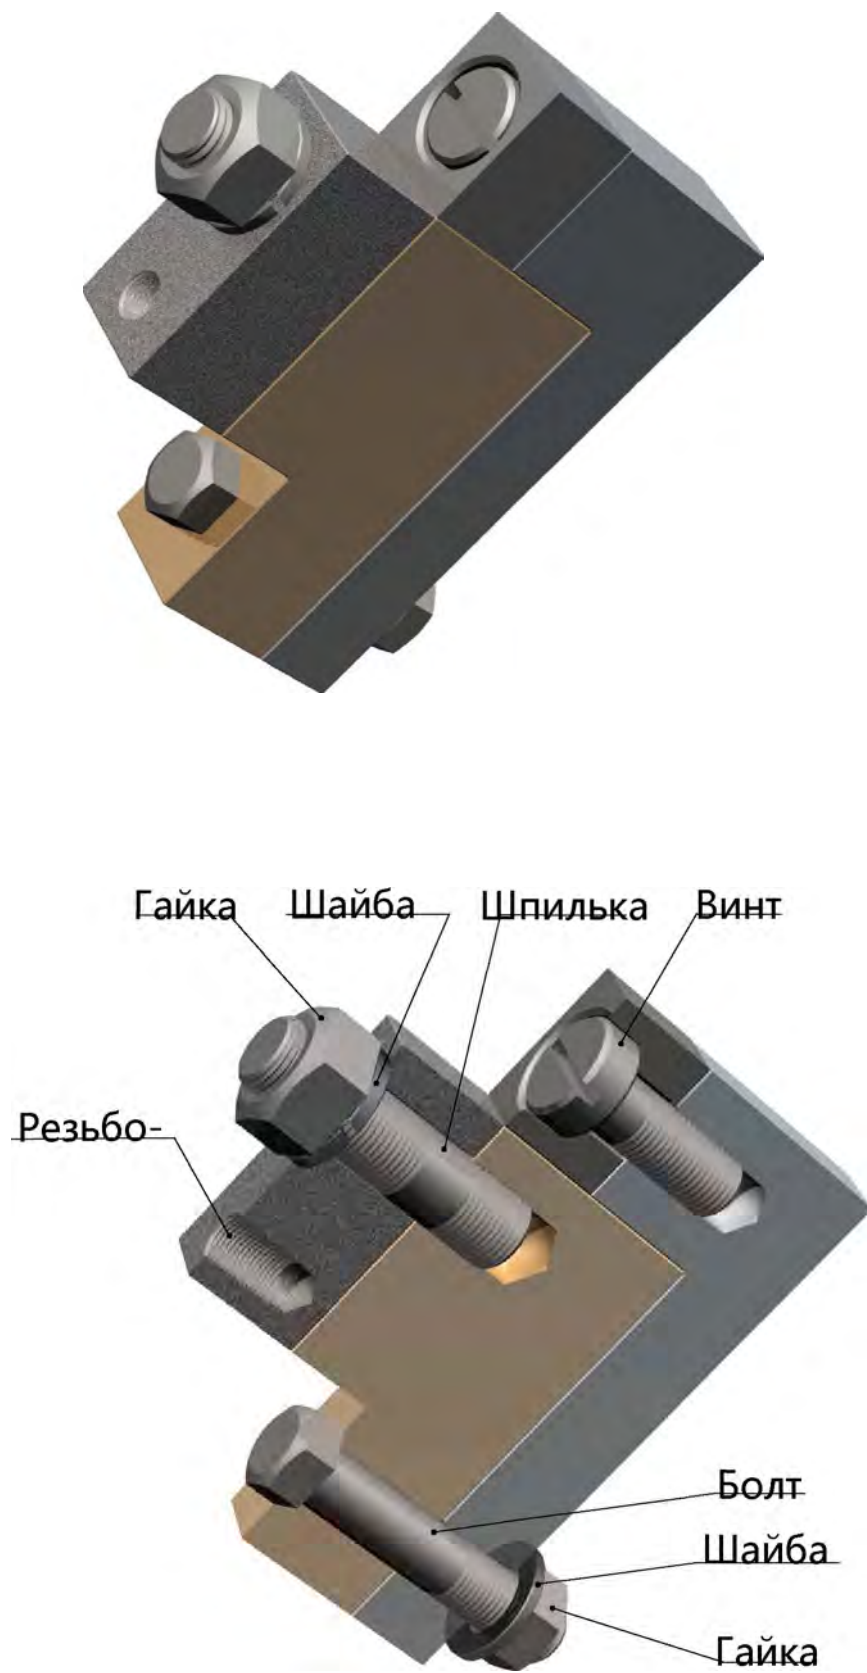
Резьбовое соединение деталей винтом с цилиндрической головкой, шпилькой с пружинной шайбой и болтом с круглой шайбой: вверху – внешний вид соединения; внизу – условный разрез соединения по осям резьбовых деталей
